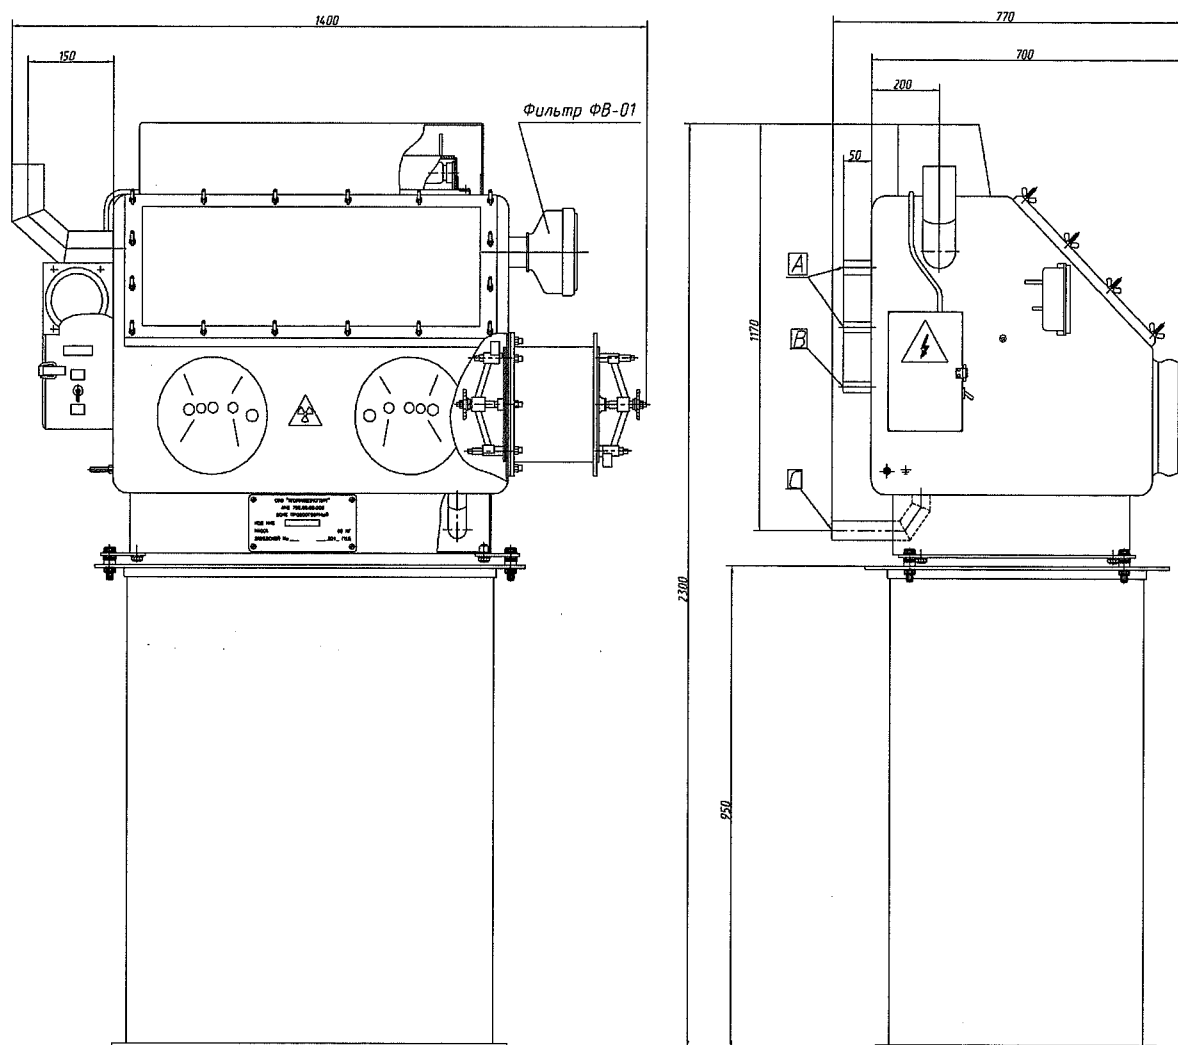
Габаритный чертеж бокса пробоотборного KUA10AX001
